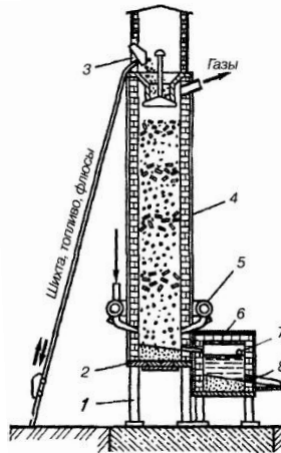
Схема вагранки с копильником: 1 - основание (колонны); 2 - лещадь (подовая плита); 3 - загрузочное окно; 4 - шахта; 5 - воздушный коллектор; 6 - копильник; 7 - отверстие для выпуска шлака; 8 - лётка для выпуска чугуна
